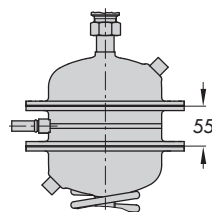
· Disegni dimensionali , valvola Tipo 2422 con soffiello di bilanciamento
